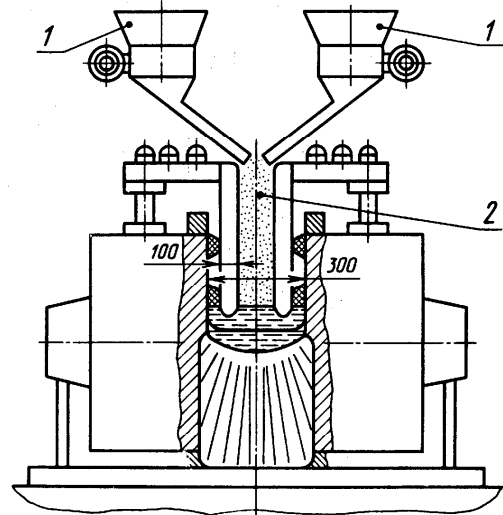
Электрошлаковая сварка заготовки вала с дополнительной подачей металлического порошка
